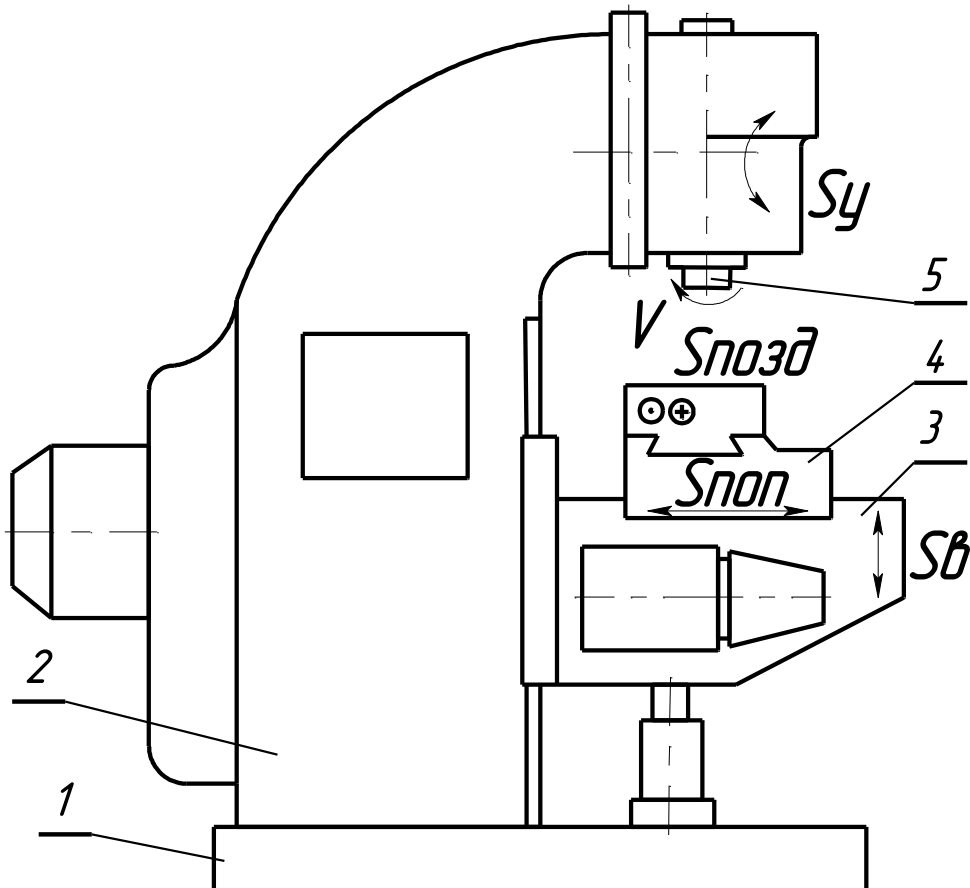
Загальний вигляд вертикально-фрезерного верстата
